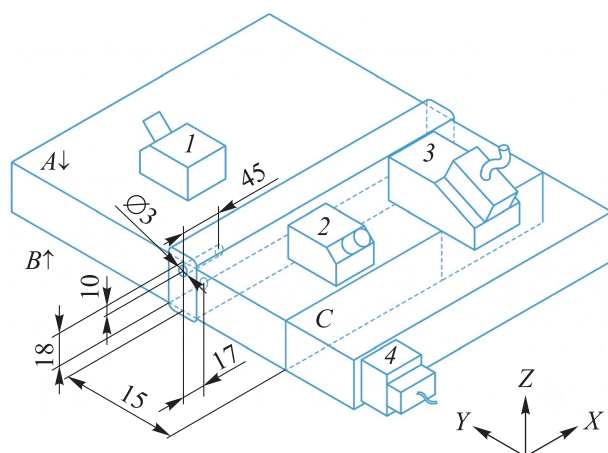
Схемы сканирования сварного шва, выполненного контактной стыковой сваркой оплавлением
